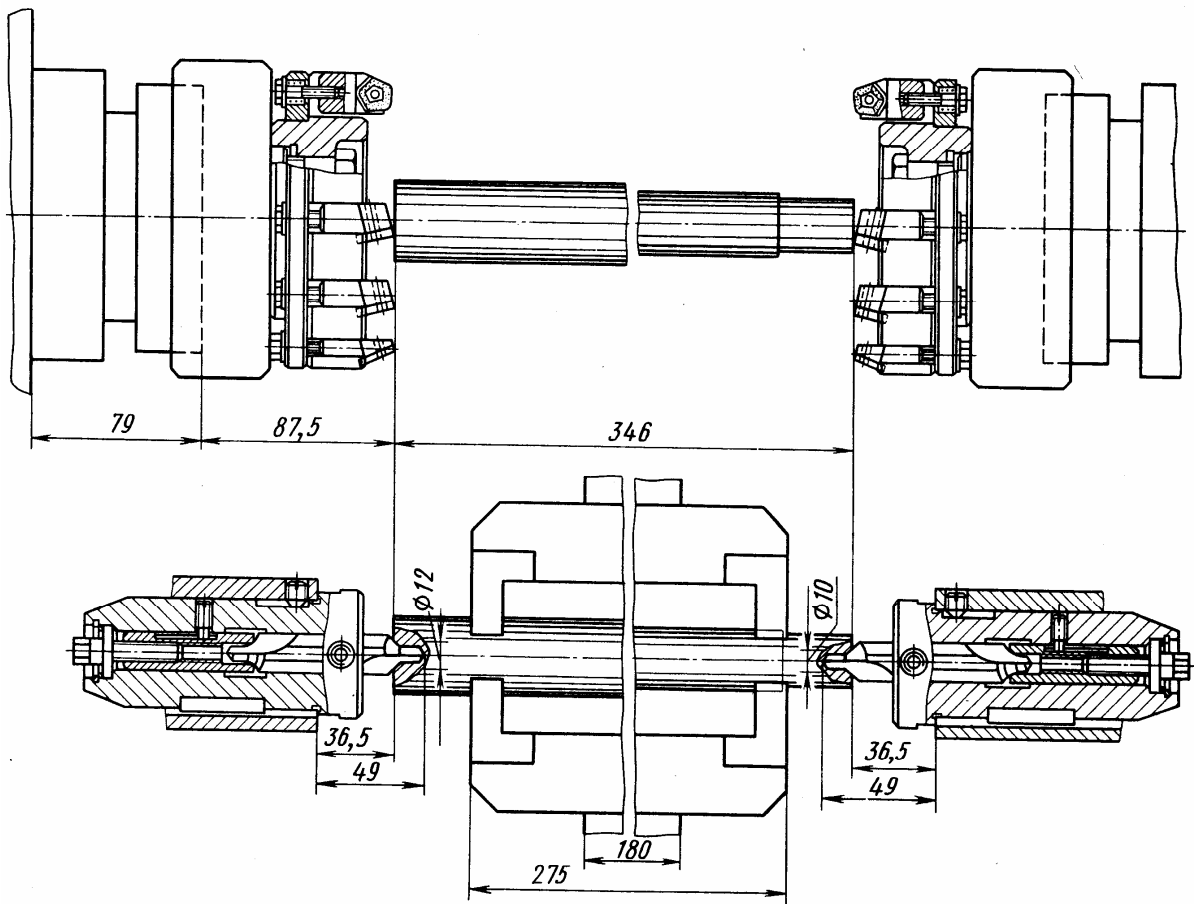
Схема налагодження фрезерно-центрувального верстата
